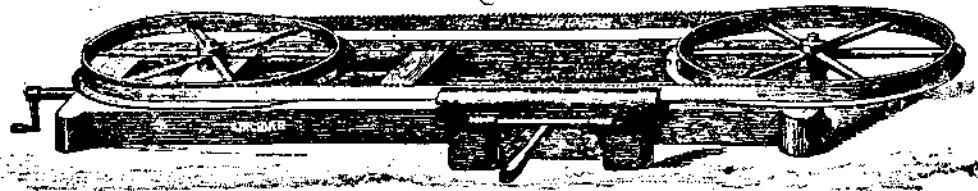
Прибор для закрепления ленточных пил при отточке и разводе зубьев.
